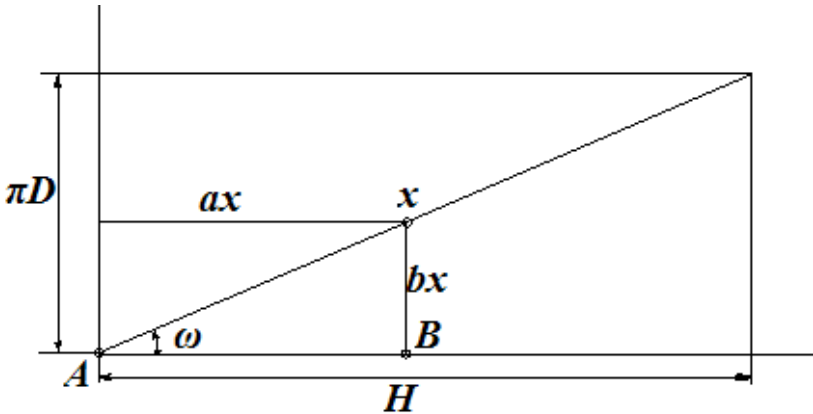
Розгортка гвинтової лінії циліндричної фрези
